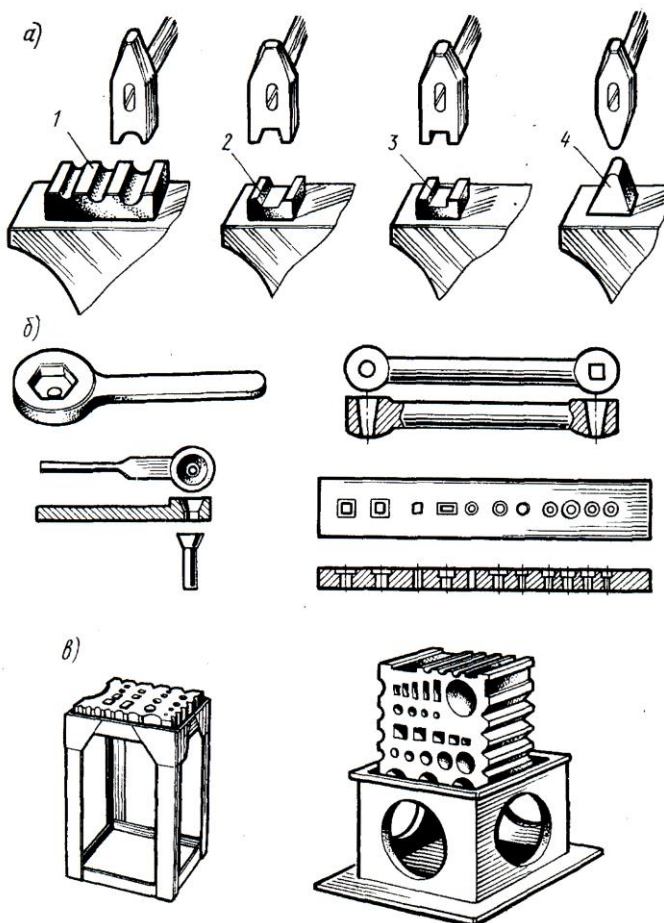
Подкладной инструмент третьей группы: а - обжимки (1 - цилиндрические; 2 - шестигранные; 3 - квадратные; 4 - подбойка); б - различные гвоздильни; в - кузнечная форма
